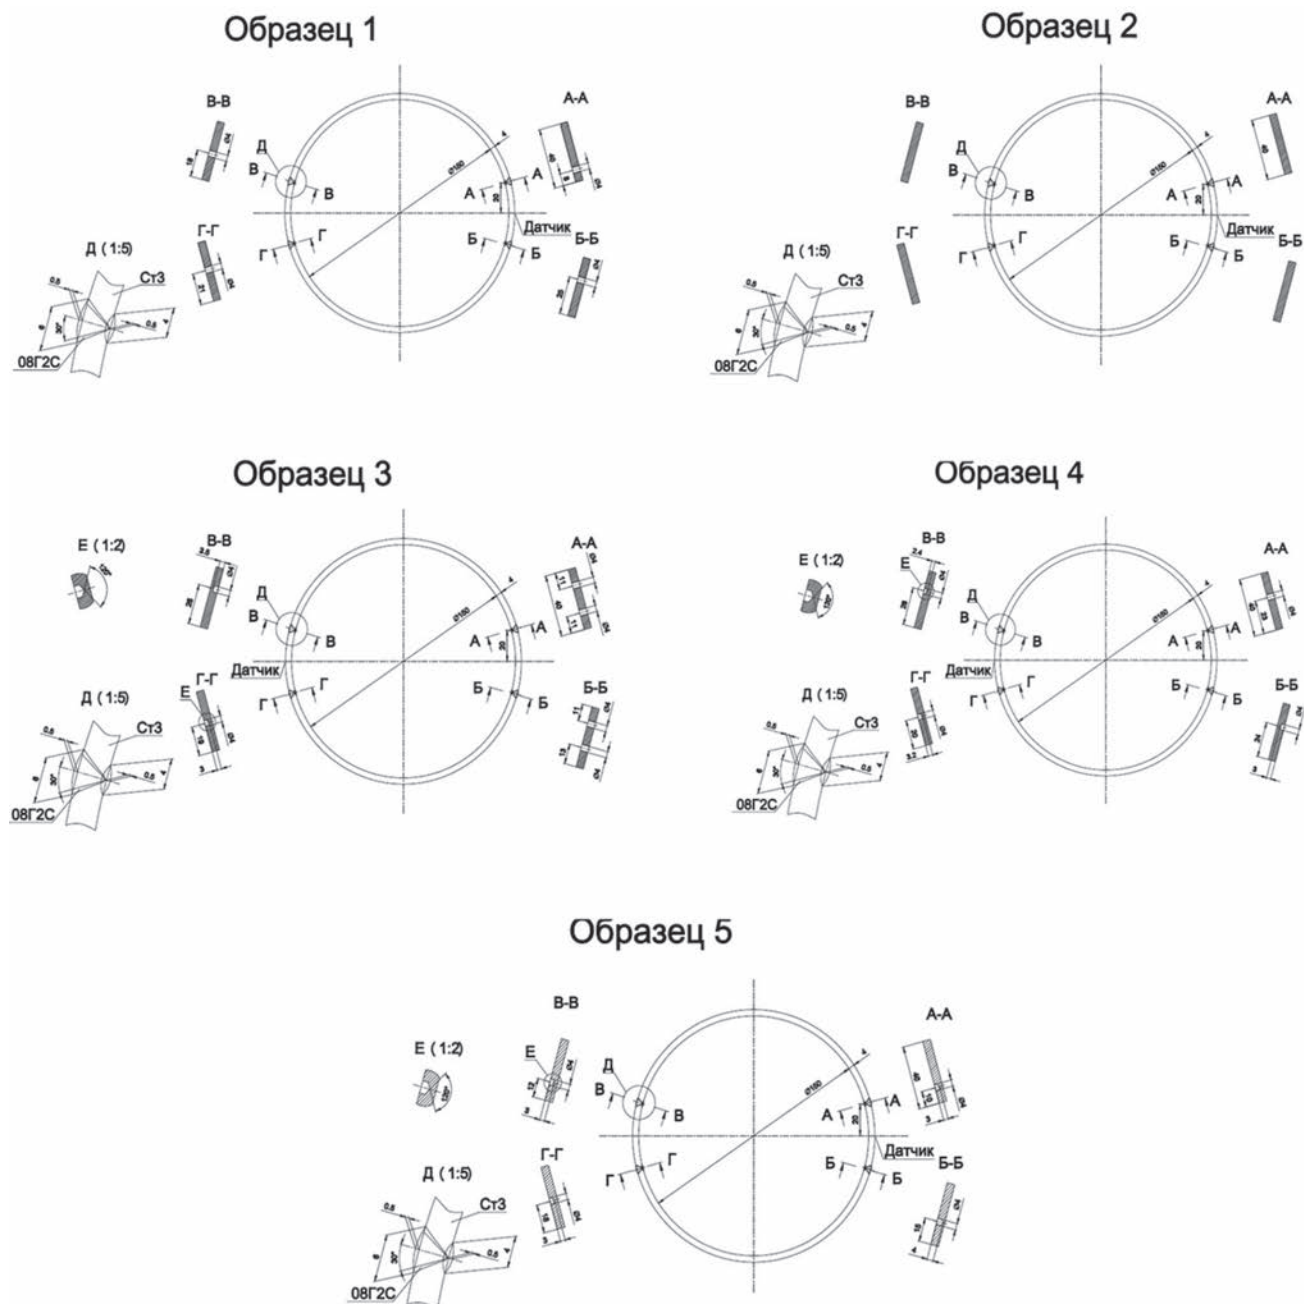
Образцы сваренных встык колец для АЭ испытания при одноосном сжатии
